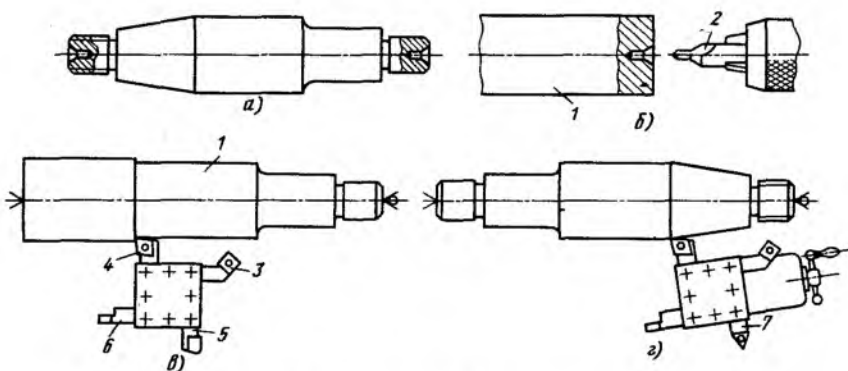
Схема обработки вала на токарно-винторезном станке:
